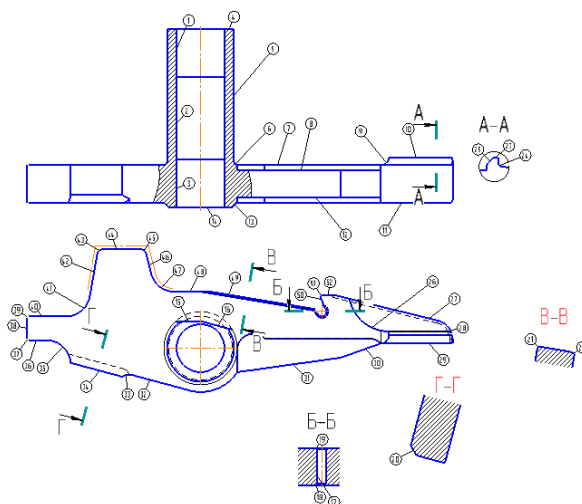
Эскиз обрабатываемых поверхностей.
